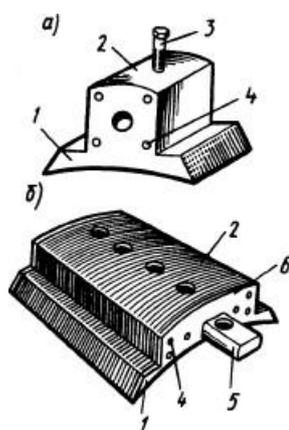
Устройство главных полюсов (а, б): 1 – полюсный наконечник; 2 – сердечник полюса; 3 – установочный болт; 4 – заклепки; 5 – установочный стержень; 6 – нажимные щетки
